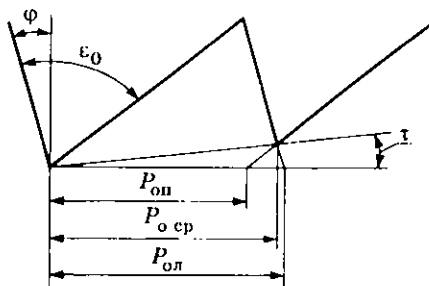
Размеры зубьев фрезы в осевом сечении
